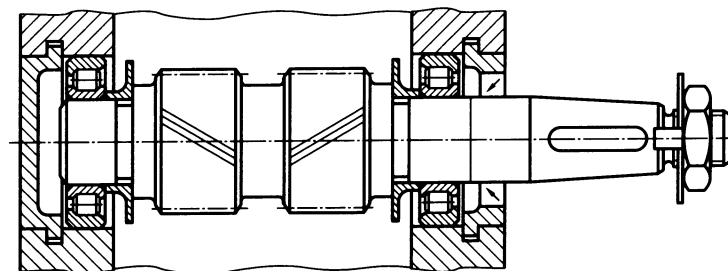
Входной вал шевронной цилиндрической передачи
